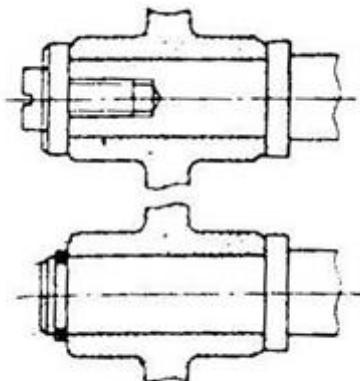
Пружинное разрезное кольцо для упрощения автоматической сборки
